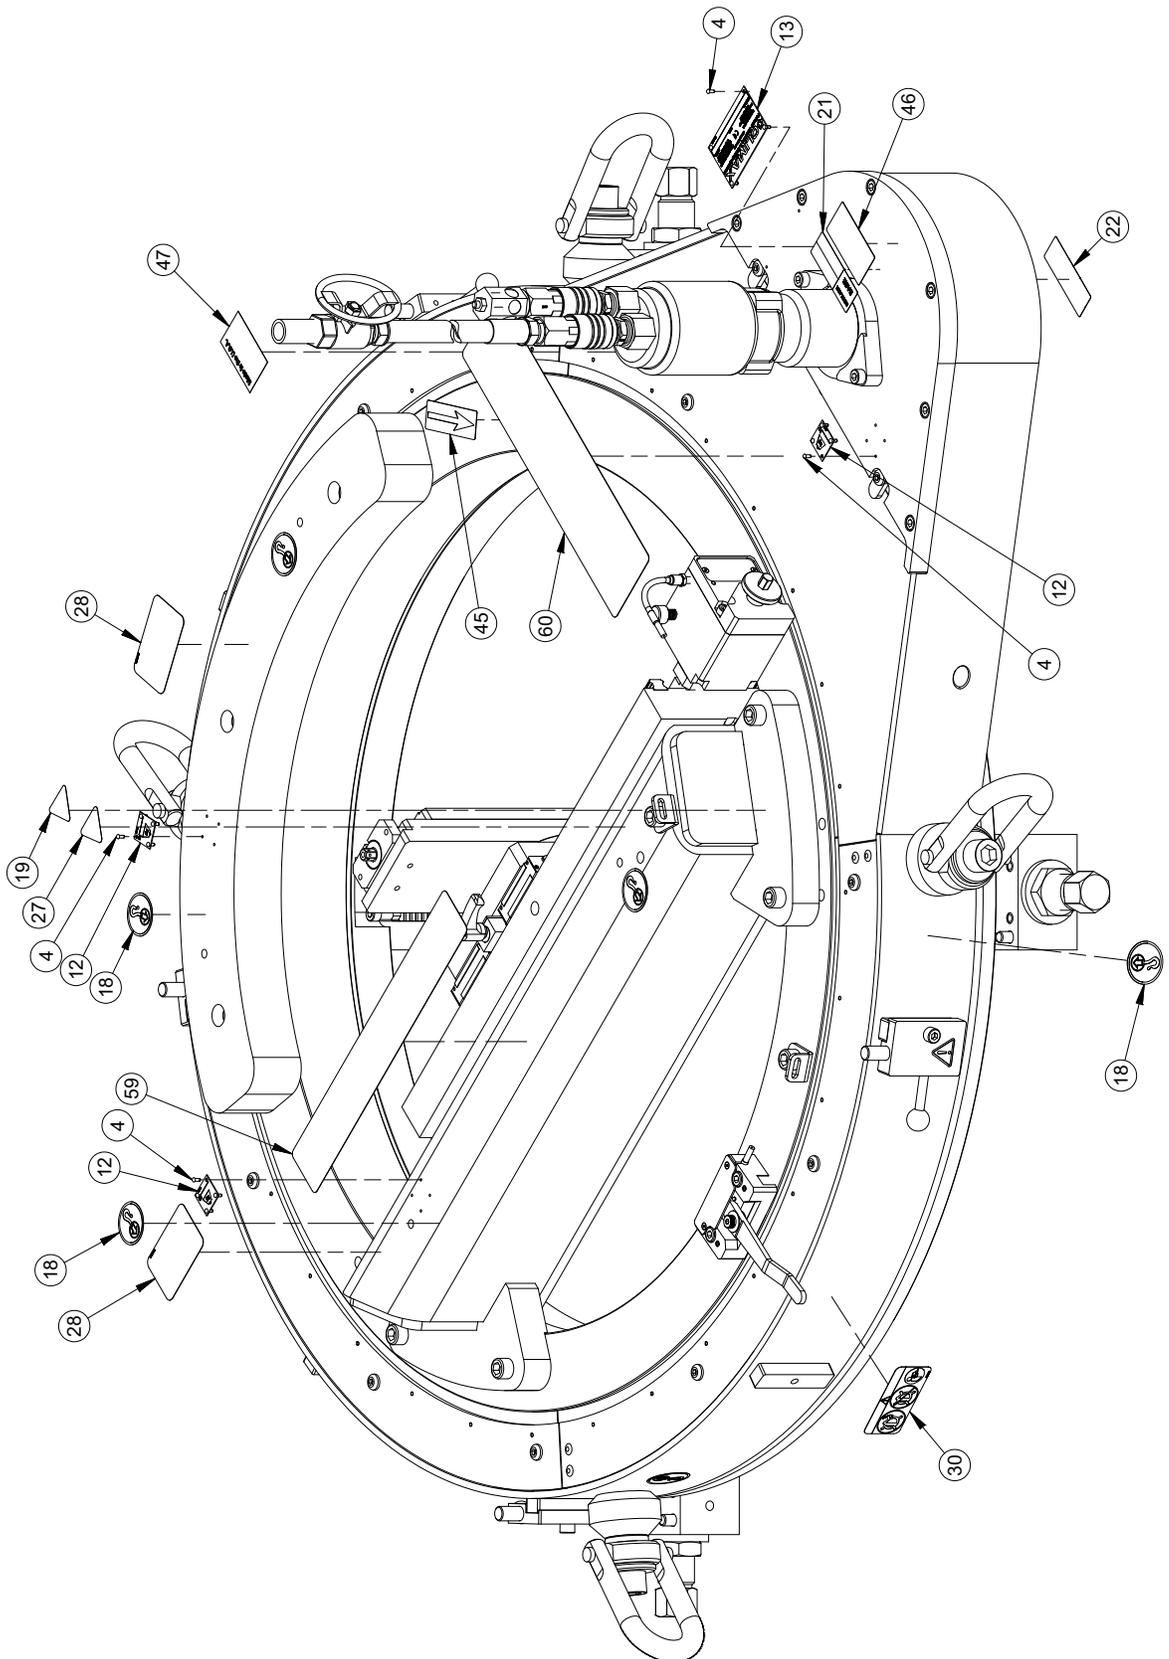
ENSEMBLE DES ÉTIQUETTES DE LA MACHINE ODF30 SPEED FACER (RÉF. 88930)
